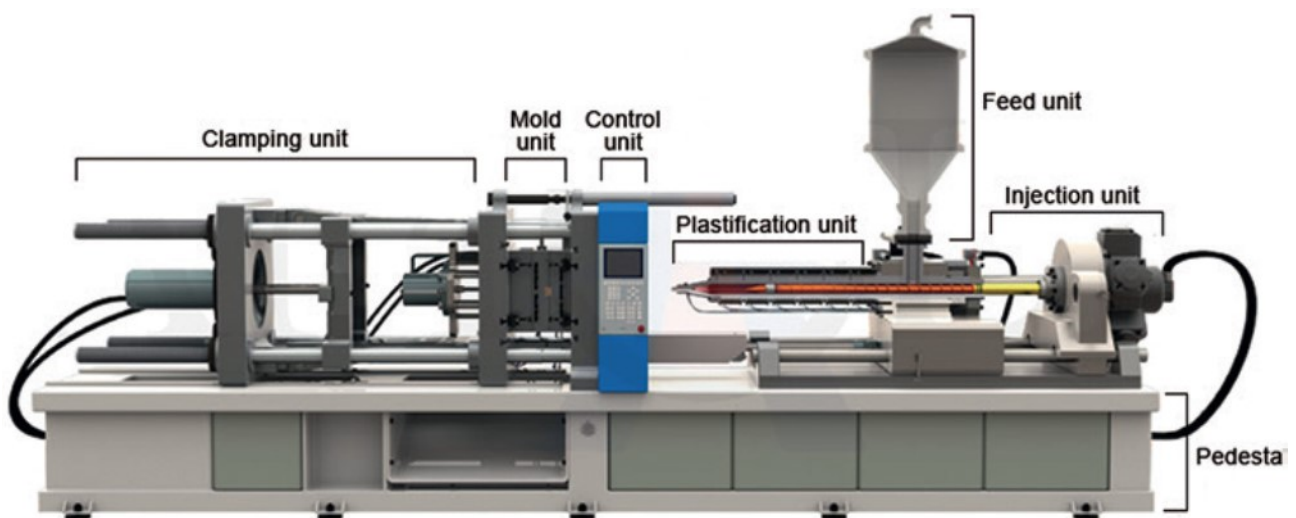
Macchinario per lo stampaggio ad iniezione.
